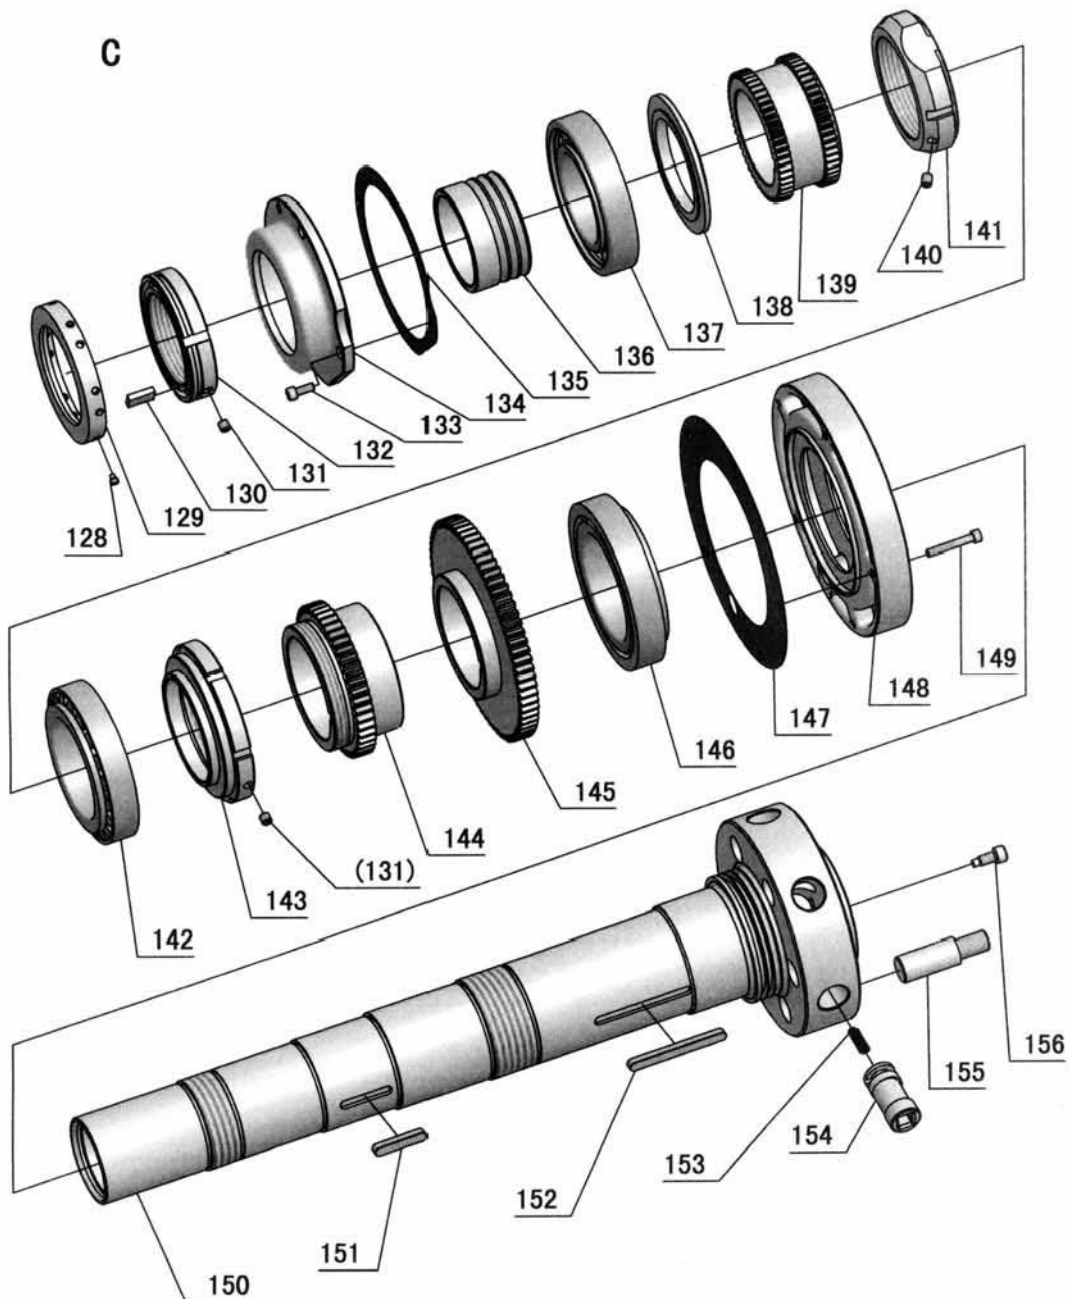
Spindelstock 5 von 8 - Headstock 5 of 8
